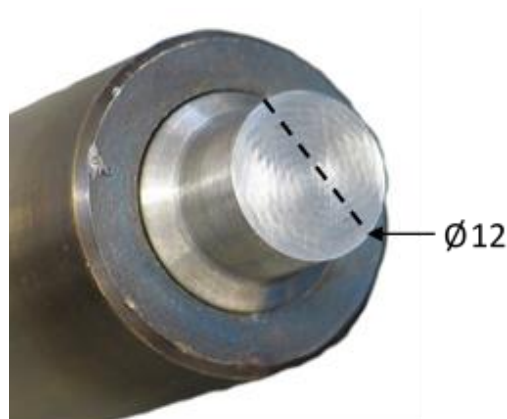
Ferramenta utilizada na produção das soldaduras por TAFSW
